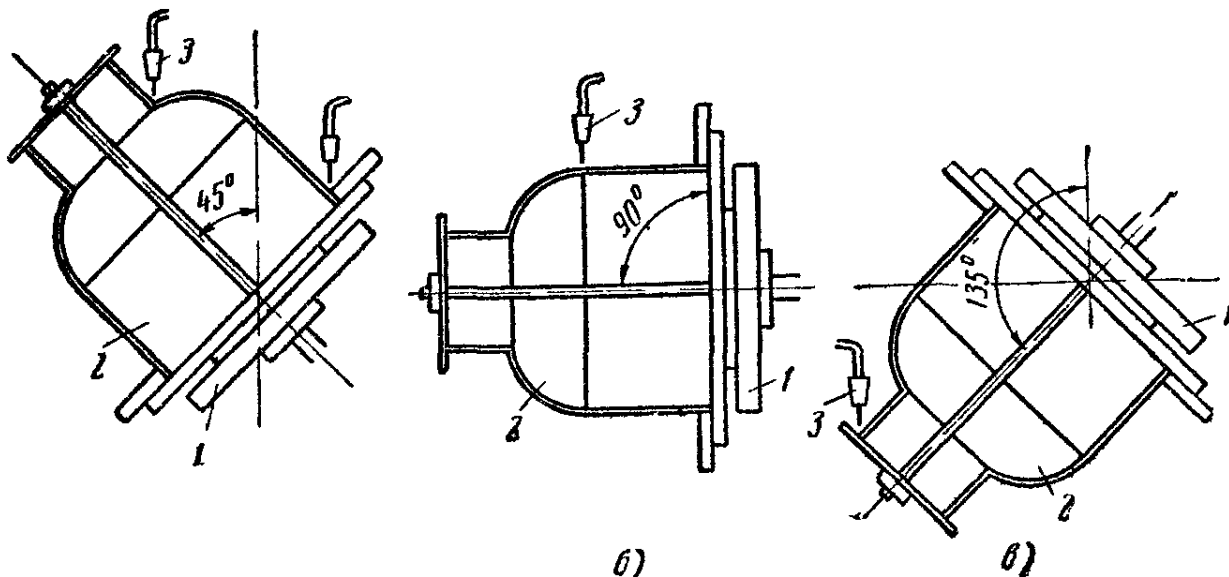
Схема положений изделия при сварке на манипуляторе:
